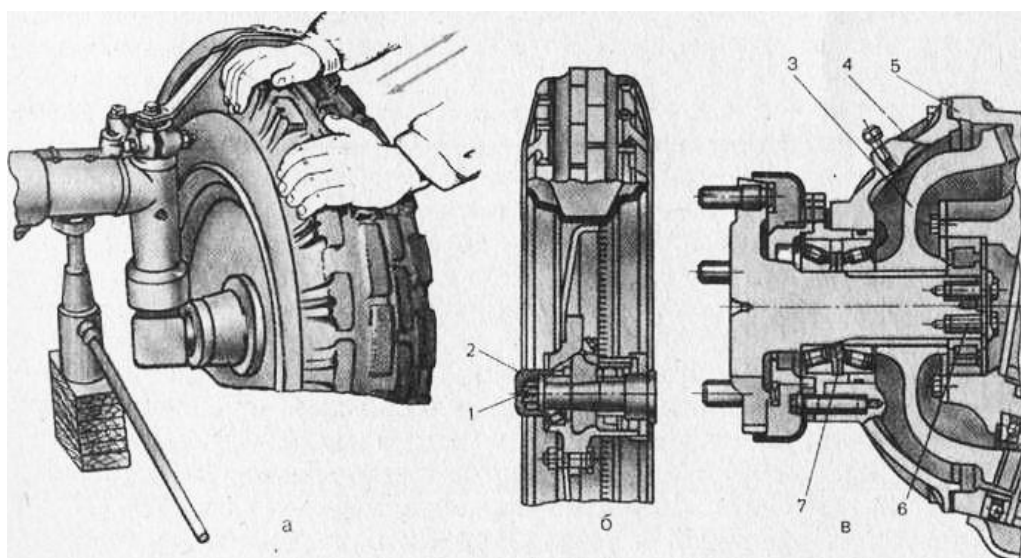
Проверка подшипников передних колес (а) и регулировки направляющего (б) и ведущего (в) колес:
